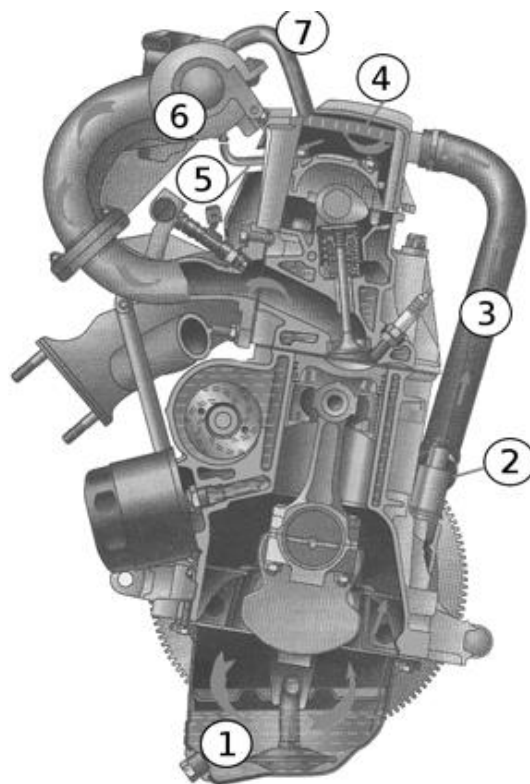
Схема вентиляции картера двигателя ВАЗ 2111:
